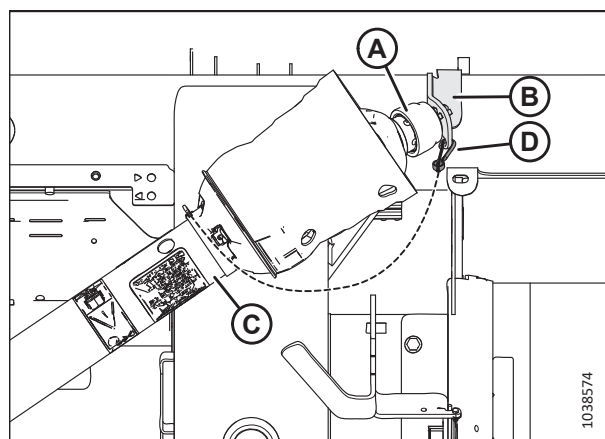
Додатковий щиток приводного вала для роботи на схилах
